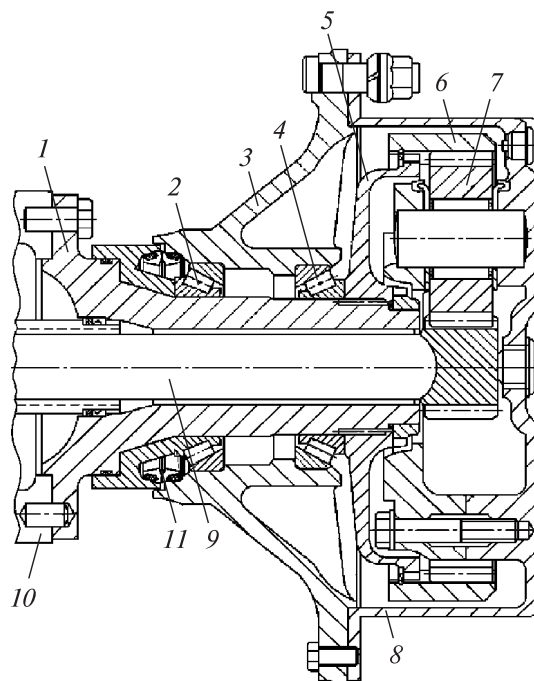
Планетарный редуктор конечной передачи моста AMK-03: 1 — цапфа; 2, 4 — ступичные подшипниковые опоры; 3 — картер планетарного редуктора; 5 — шлицевая втулка; 6 — эпициклическое колесо; 7 — спутник; 8 — водило; 9 — выходной вал гитары; 10 — картер гитары; 11 — уплотнение конечной передачи
